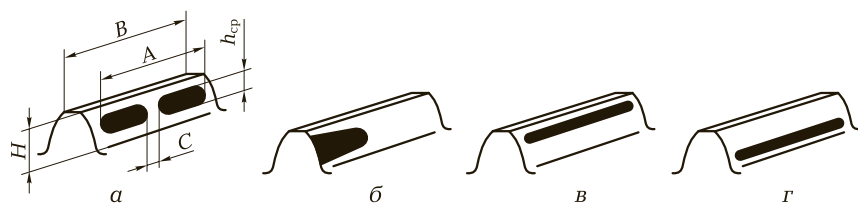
Контроль прямозубых цилиндрических зубчатых колес по расположению пятна контакта:
